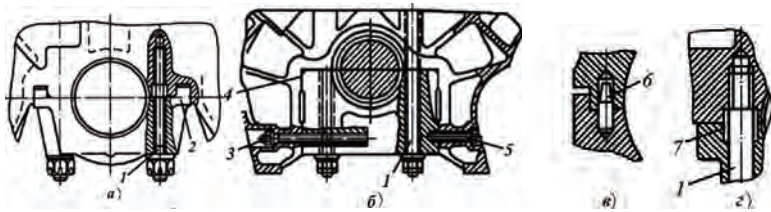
Крепление крышек коренных подшипников коленчатого вала с использованием фиксирующих элементов: а – выступ; б – поверхностей и стяжных шпилек; в – штифтов; г – втулок; 1 – основная силовая шпилька; 2 – фиксирующие выступы крышки; 3 – стяжная сквозная шпилька; 4 – фиксирующая поверхность; 5 – стяжной болт; 6 – штифт; 7 – втулка
